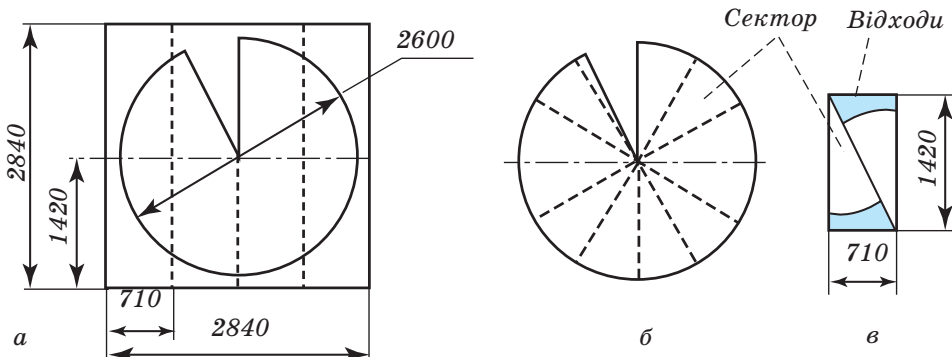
Схеми розкроювання заготовок для конічної поверхні:
